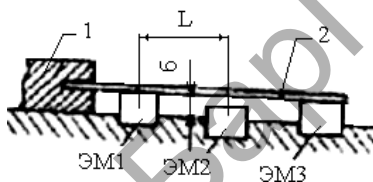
Схема привода микроперемещения салазок токарного станка
